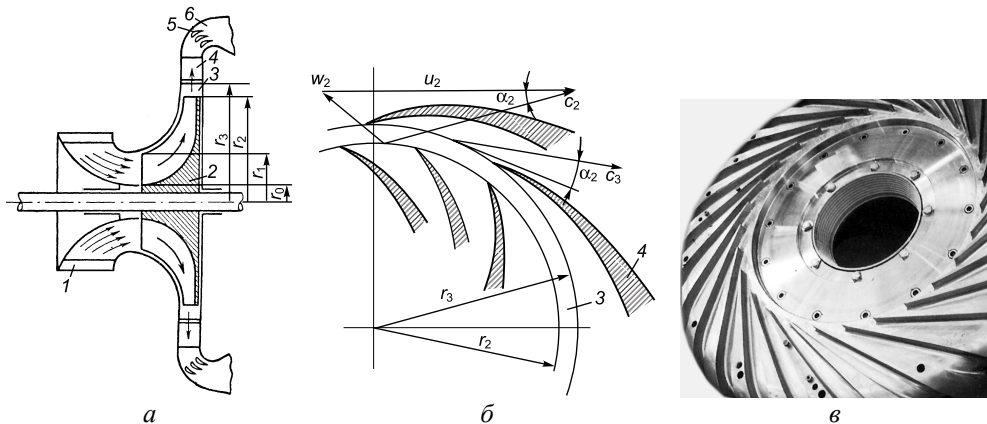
Ступень центробежного компрессора (а), схема расположения безлопаточного и лопаточного диффузоров (б) и внешний вид лопаточного диффузора ГТУ РGT2 (в): 1 – направляющий аппарат; 2 – рабочее колесо; 3 – безлопаточный диффузор; 4 – лопаточный диффузор; 5 – поворотные лопатки; 6 – диффузор.
